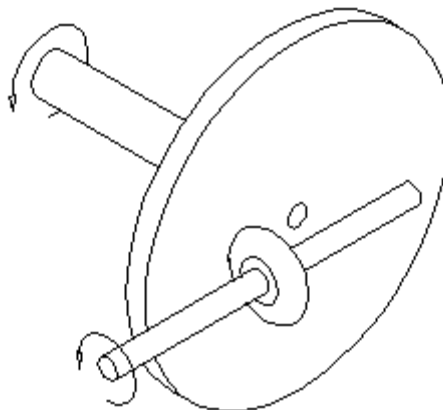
TVC com disco e roda. Adaptado de [3].
